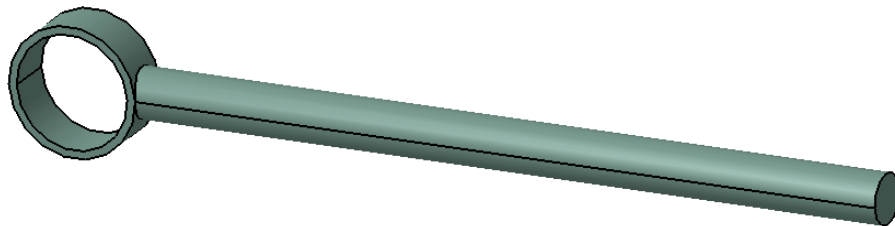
Seat mounting frame 11*: Soldadura 1 del brazo oscilante superior
